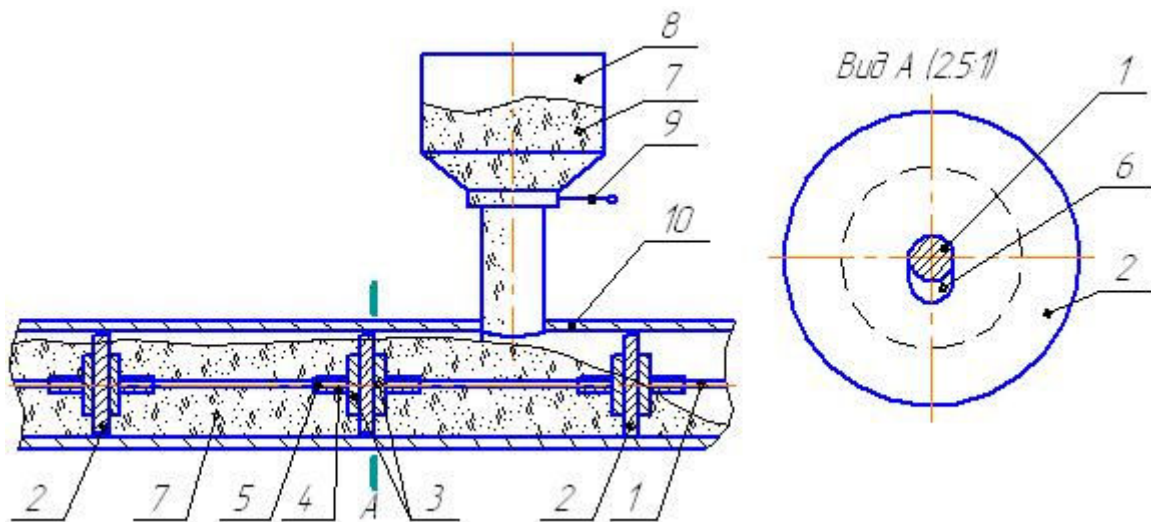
Робочий орган гвинтового канатного конвеєра
